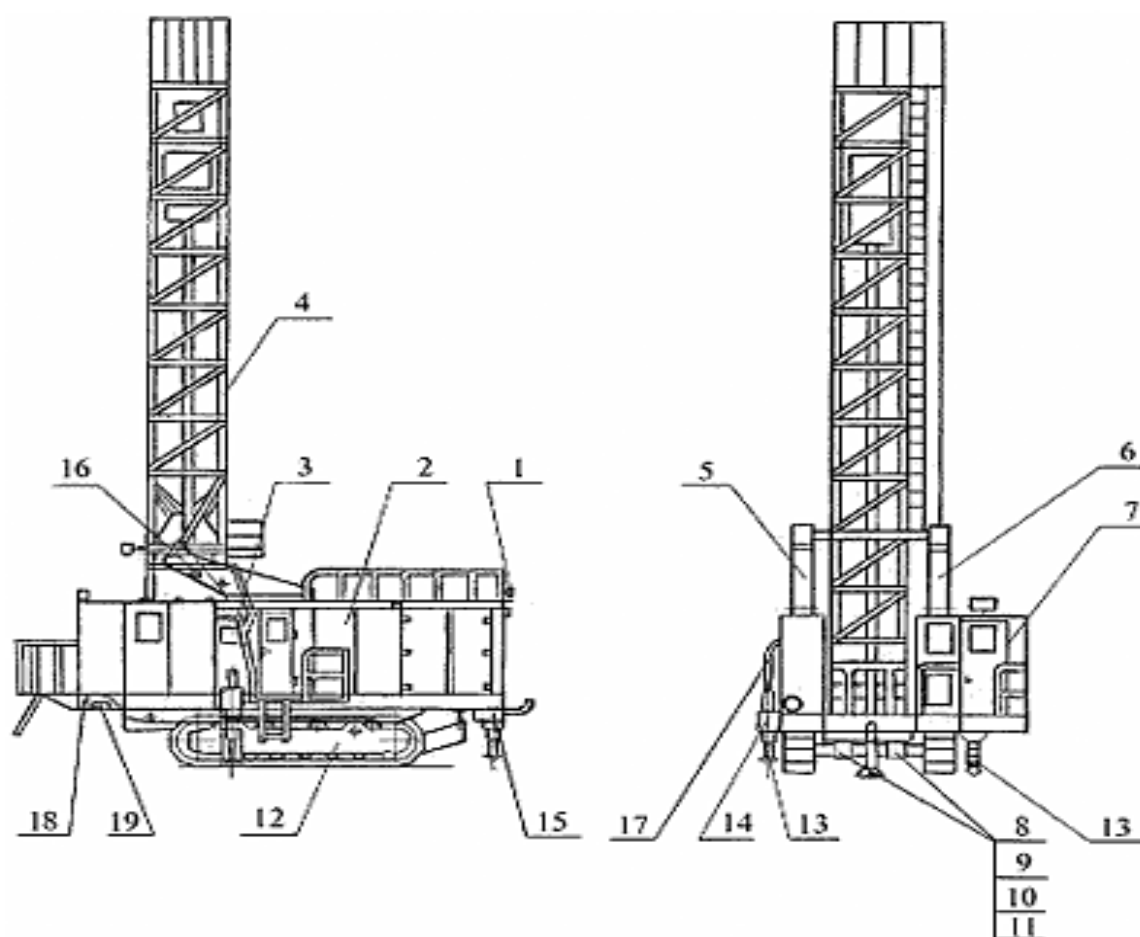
Общий вид бурового станка СБШ-250МНА-32:
